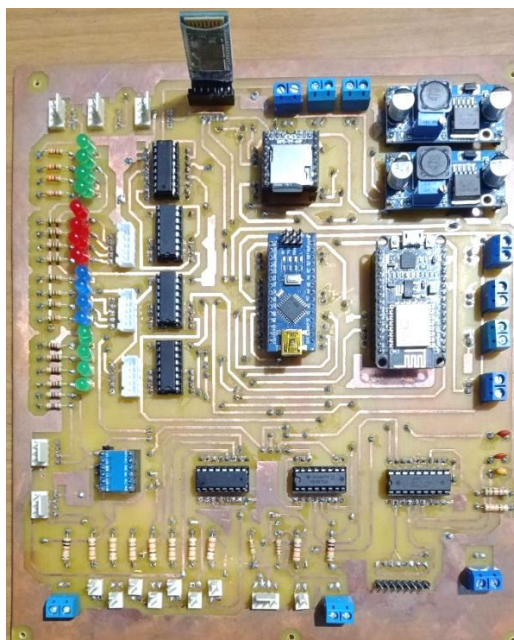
Montaje de los dispositivos electrónicos, sobre la baquelita doble cara.
